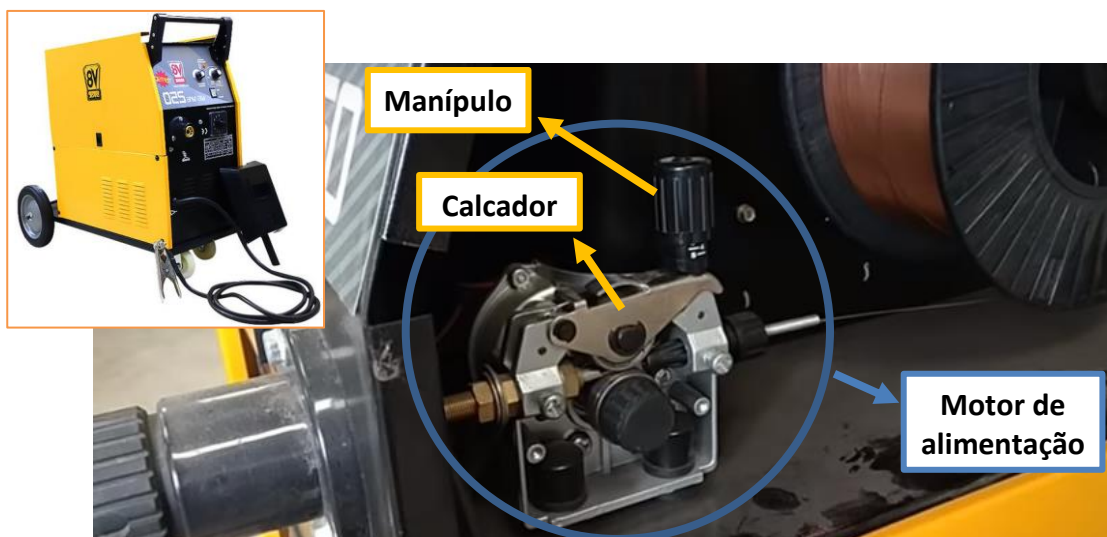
Motor de alimentação de uma máquina de soldar (Manípulo e Calcador) [Adaptado de (Torreiro, 2017)].
